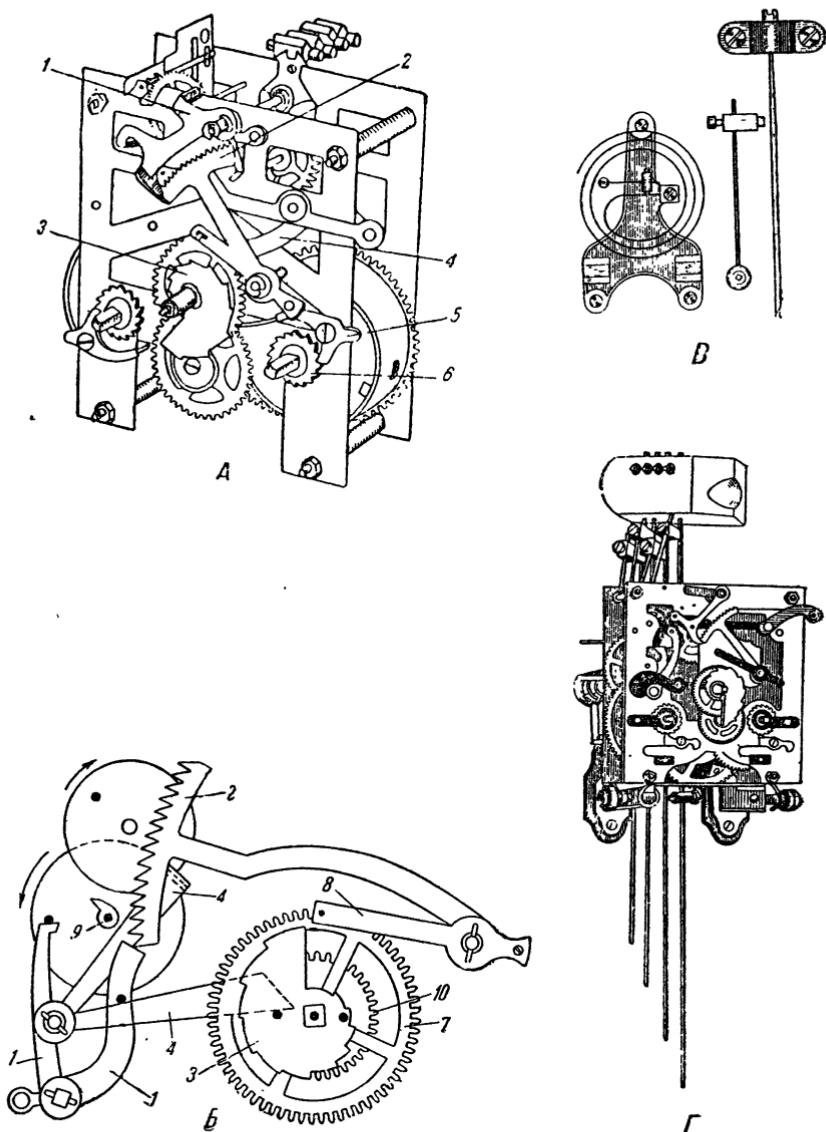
А—механизм часов с гребенкой; Б—схема работы механизма боя с гребенкой; В и Г—звукопружины; 1—рычаг замыкания; 2—гребенка; 3—ступенчатый диск; 4—рычаг отмыкания; 5—собачка; 6—храповое колесо; 7—часовое колесо; 8—колено гребенки; 9—счетный кулачок; 10—минутник
